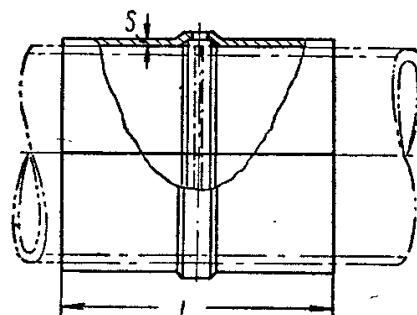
Предохранительная муфта с канавкой для валика сварного шва.
